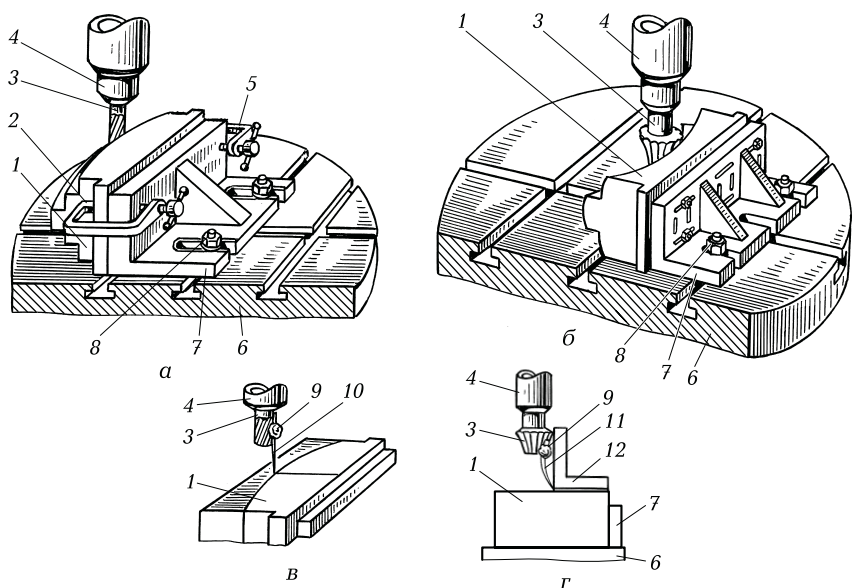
Приемы фрезерования заготовок с выпуклыми (а, в) и вогнутыми (б, г) поверхностями:
